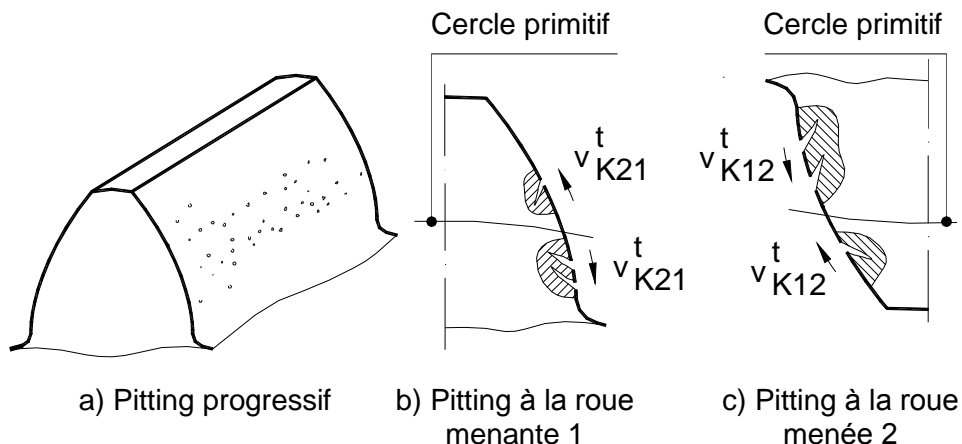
Détérioration par la fatigue de contact (pitting) des flancs
